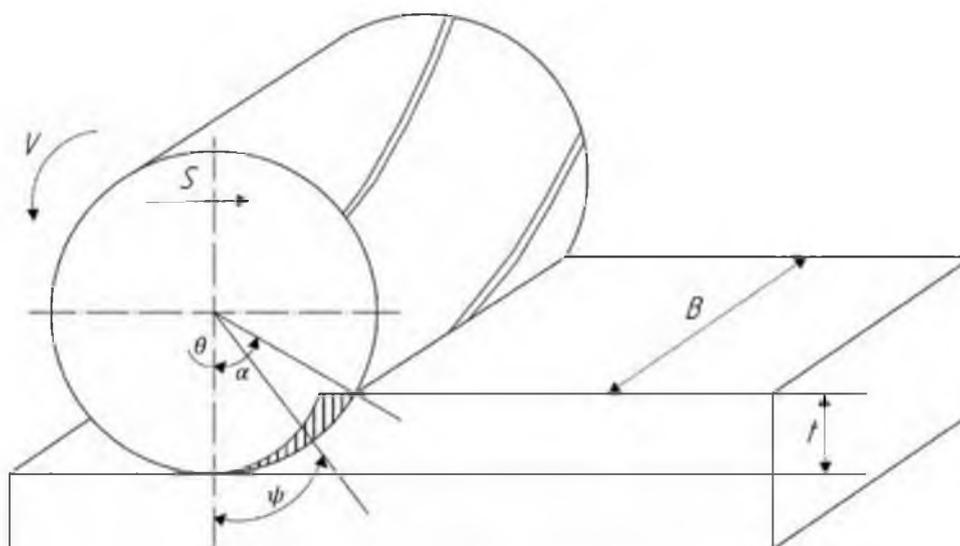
Принципиальная кинематическая схема для фрезы
